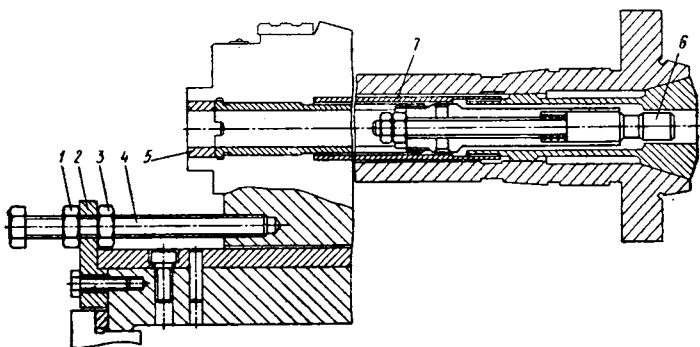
Настройка станков 1Н325 и 1Н318 для обработки штучных заготовок
